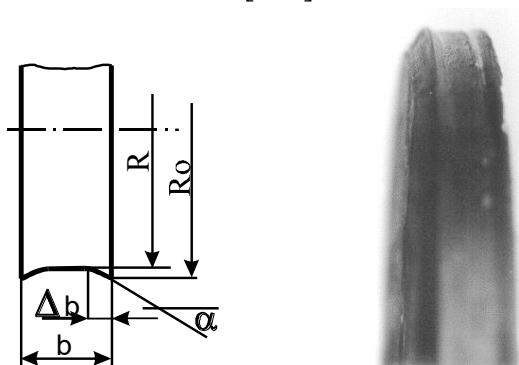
Циліндричний електрод для контактного наварювання з профільною робочою поверхнею
